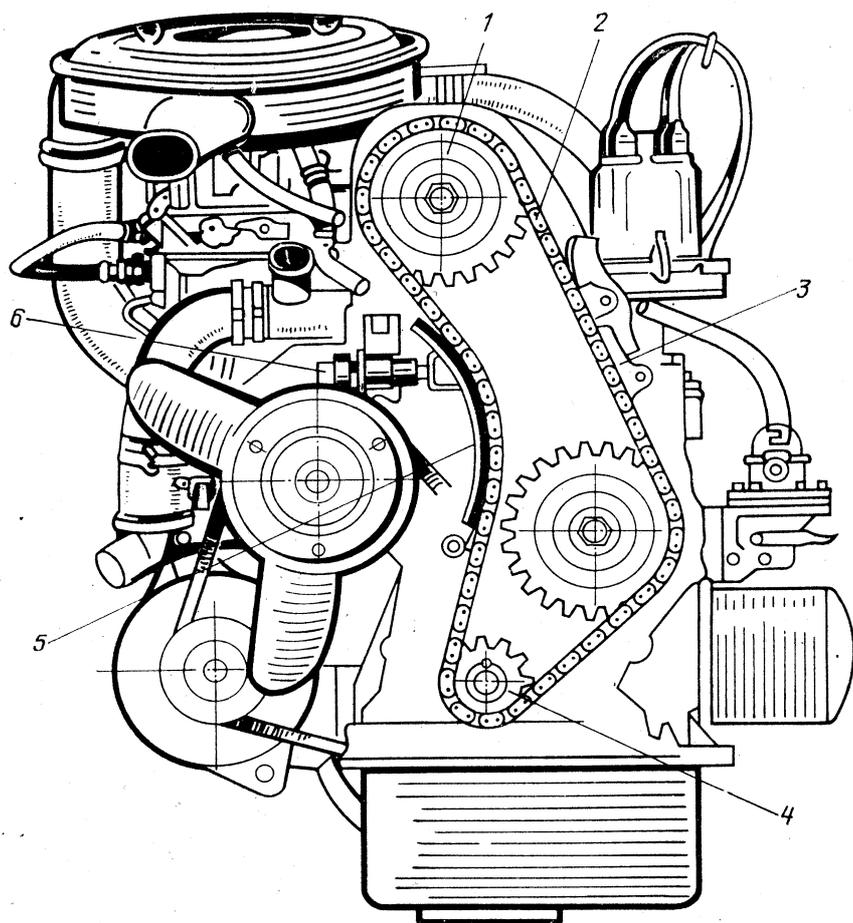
Цепной привод распределительного вала двигателя: 1 — ведомая звездочка распределительного вала; 2 — цепь привода распределительного вала; 3 — успокоитель цепи; 4 — ведущая звездочка; 5 — башмак натяжителя цепи; 6 — колпачковая гайка натяжителя цепи
